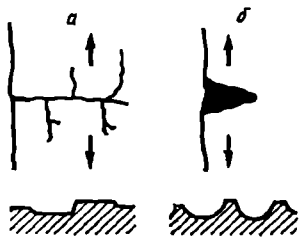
Вид трещины и схемы разрушения (сечение перпендикулярно поверхности излома):
